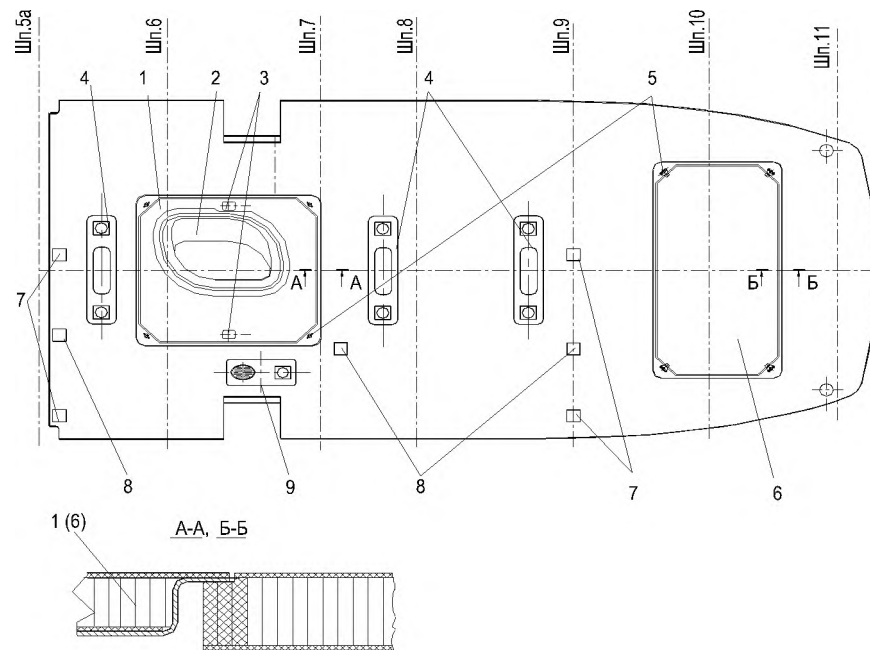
Верхняя панель кабины вертолета Ка-226А [12]:
